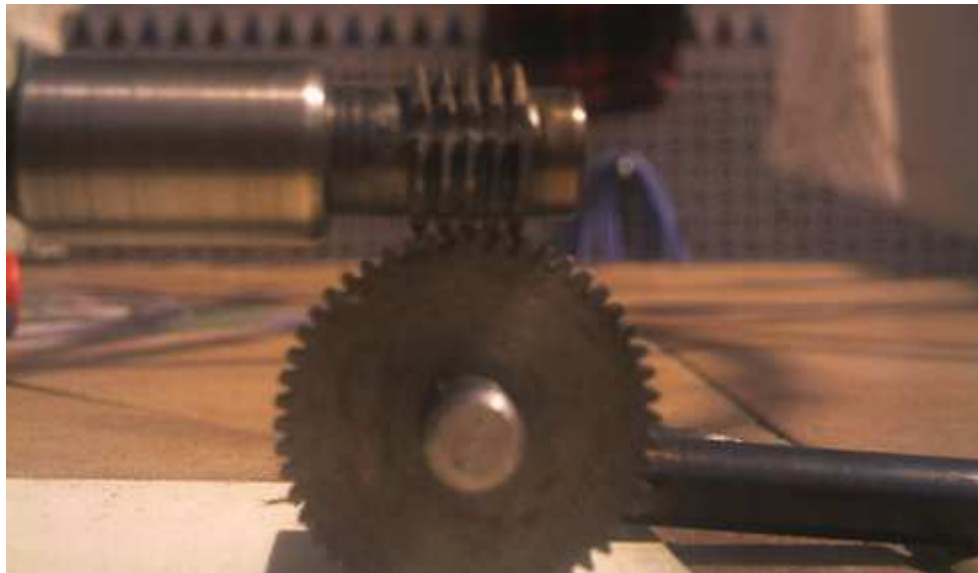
“Fresa especial de tallado de engranajes”
